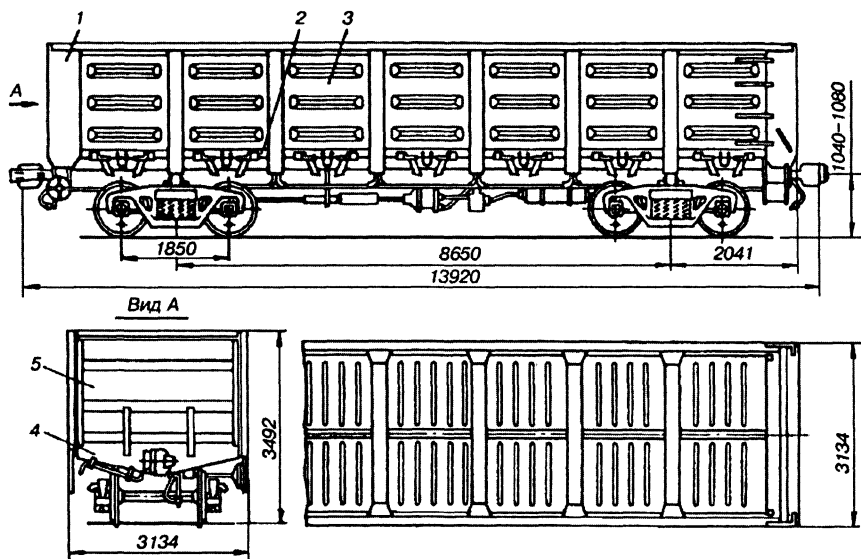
Универсальный четырехосный полувагон с глухими торцевыми стенами
